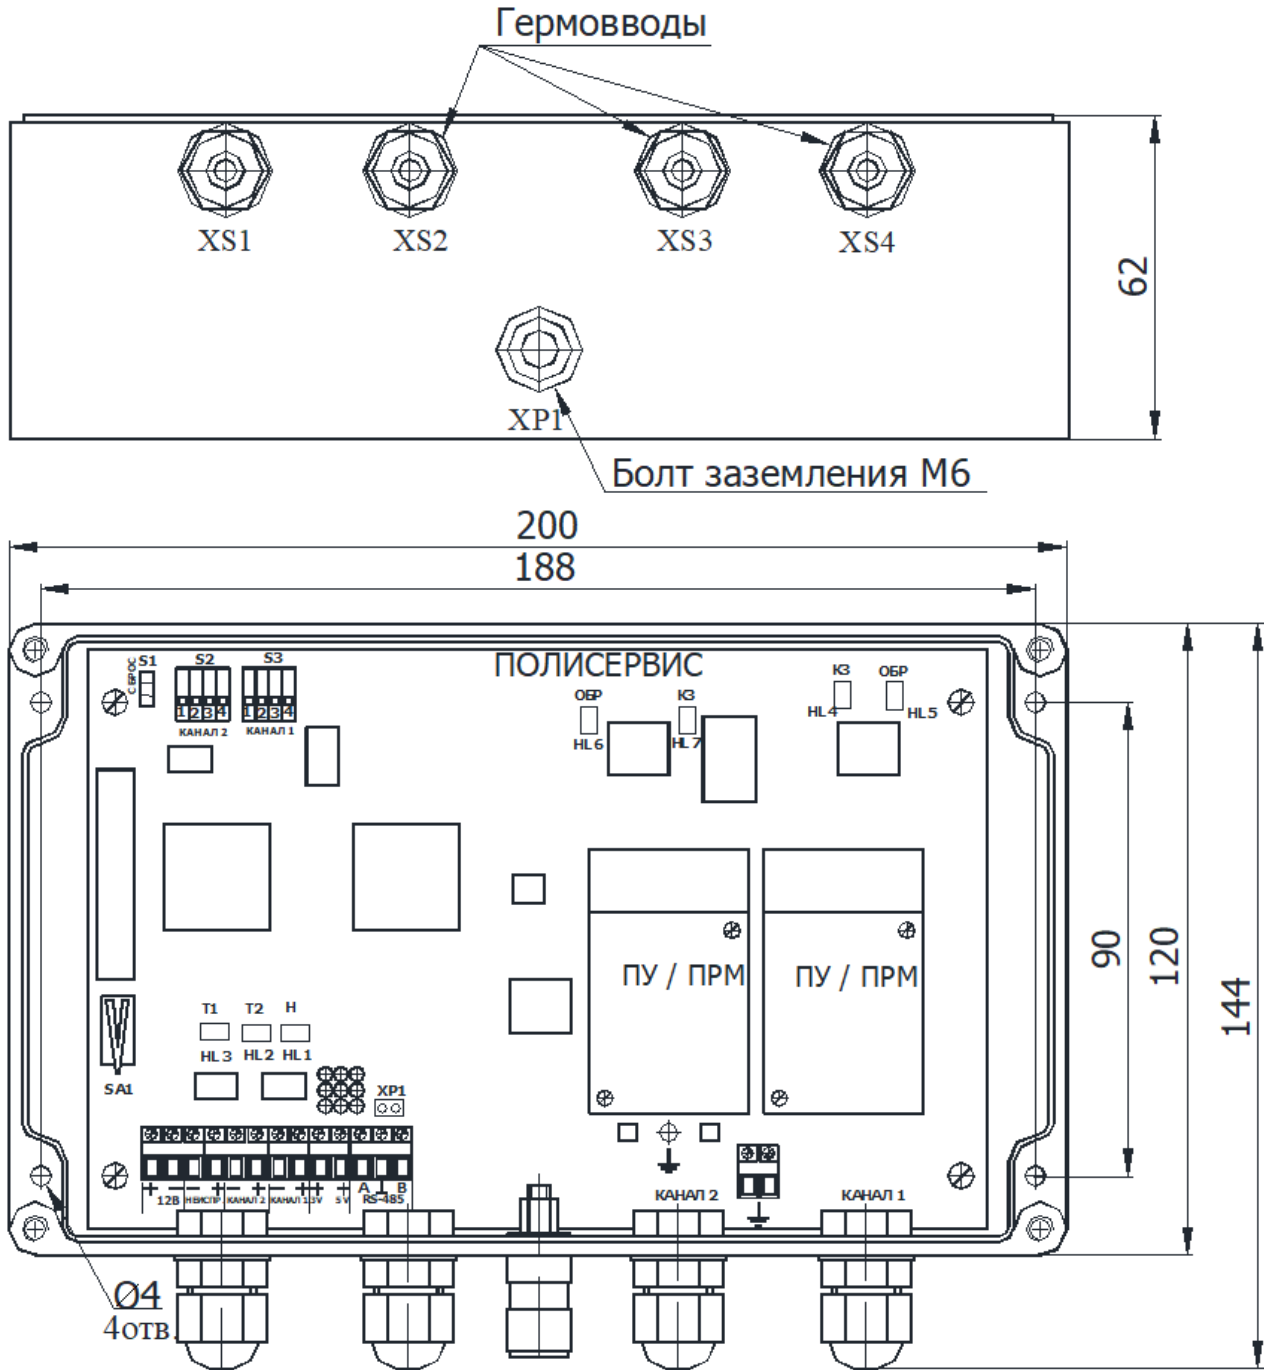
Общий вид модуля БОС в поликарбонатном корпусе со снятой крышкой и с установленными модулями (ПУ / ПРМ)
